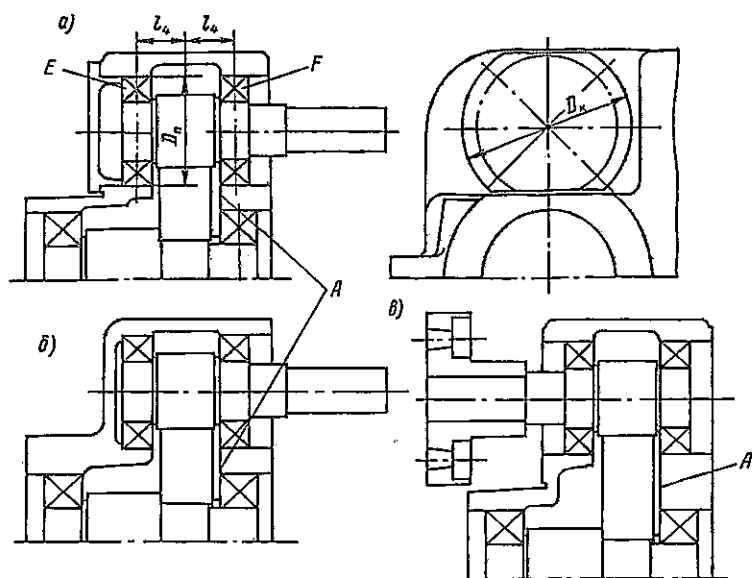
Примеры компоновки шестерни быстроходной ступени, вынесенной из плоскости разреза корпуса
